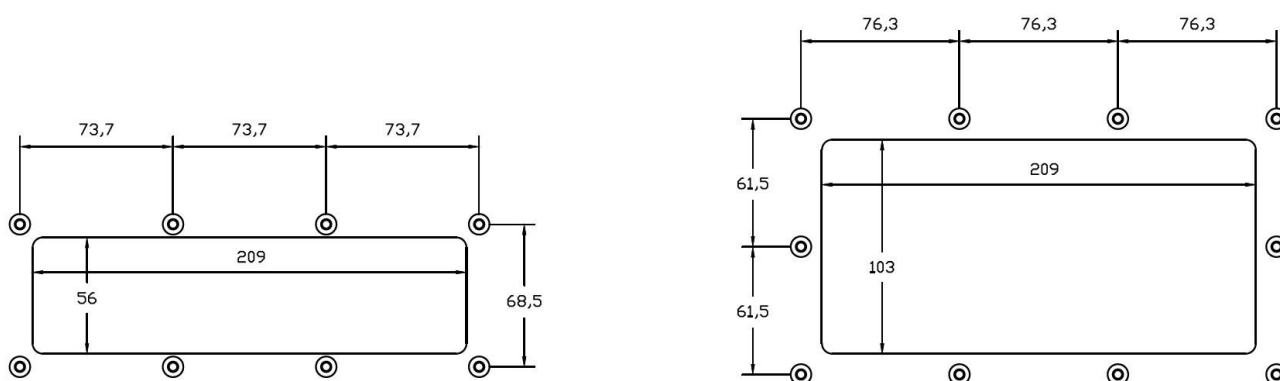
dettaglio aperture e fori sulla piastra di fondo dell'armadio per montaggio kit Roxtec
